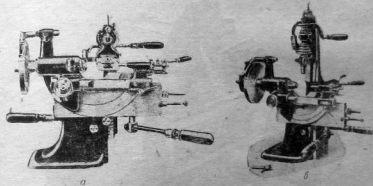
Универсальный фрезерный станок Дикси с вертикальным столом.
